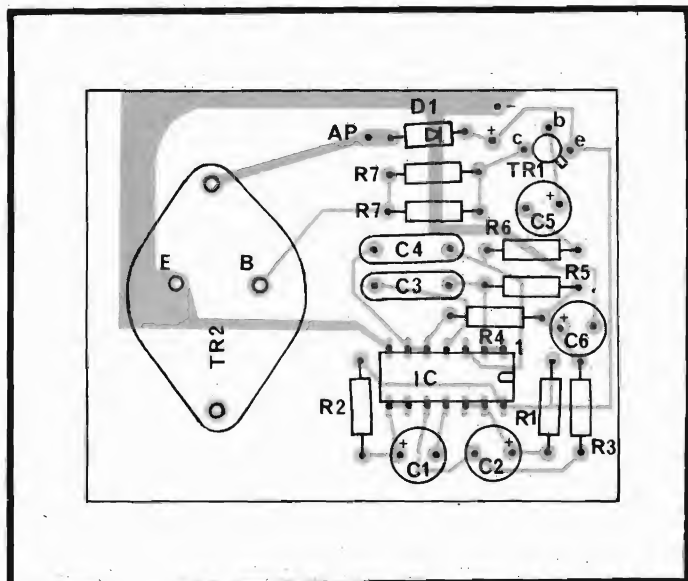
Disposizione dei componenti sulla basetta vista in trasparenza.
